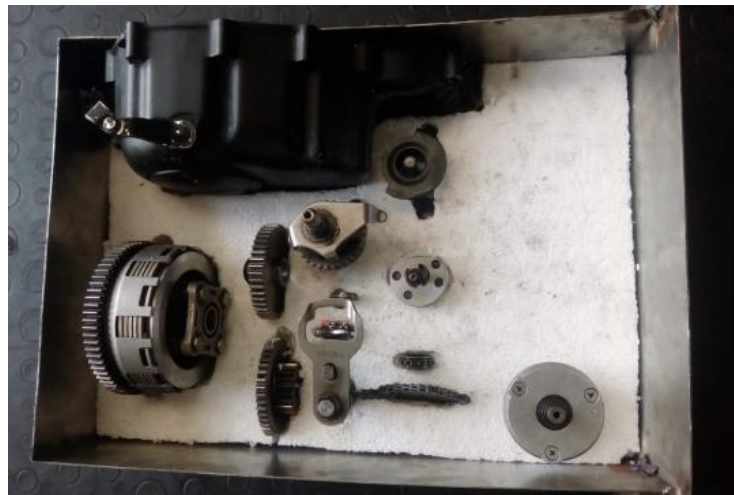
Acoplamiento de Piezas al Molde de Icopor
